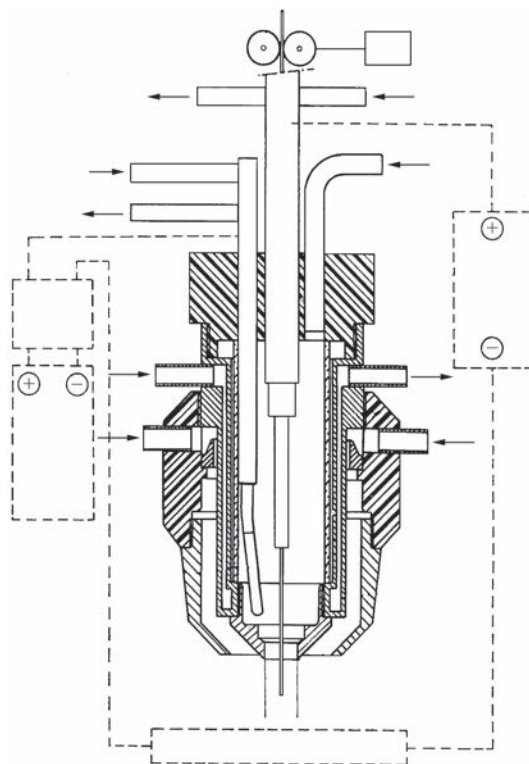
Плазматрон для гибридной плазменно-дуговой сварки плавящимся электродом, разработанный фирмой Philips Corporation [2]
